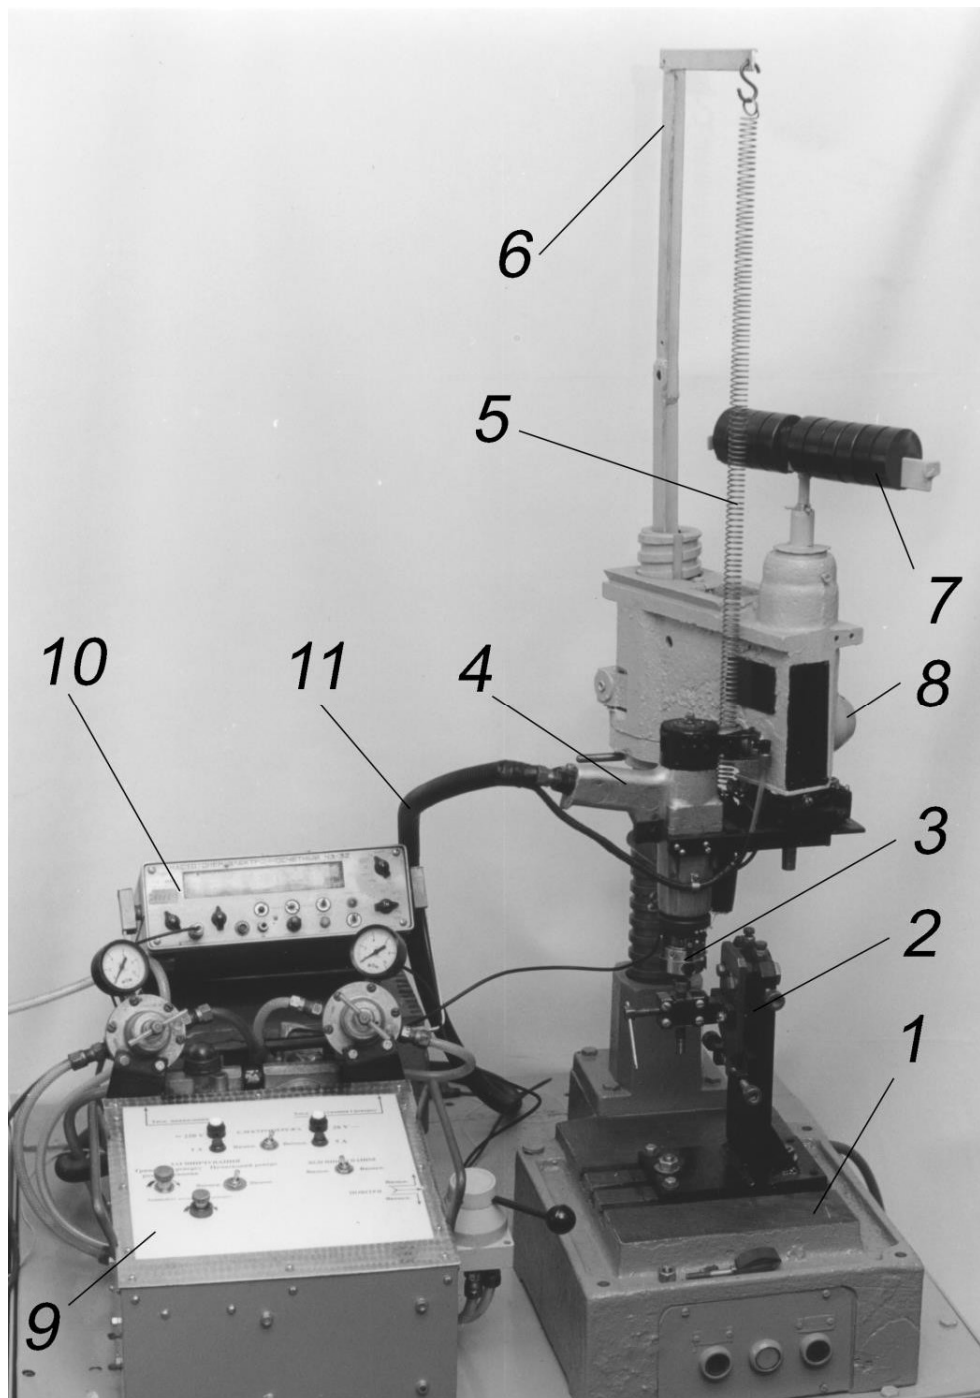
Зовнішній вигляд експериментальної установки: 1- станина; 2- пристрій для базування шпильки; 3- головка з податливою базою гайки; 4- пневматичний адаптивний гайкокрут; 5- зрівноважувальна пружина; 6- кронштейн пружини; 7- тягарці; 8- механізм ручного переміщення гайкокрута; 9- пульт керування; 10- частотомір; 11- джгут із пневмоелектропроводів.
